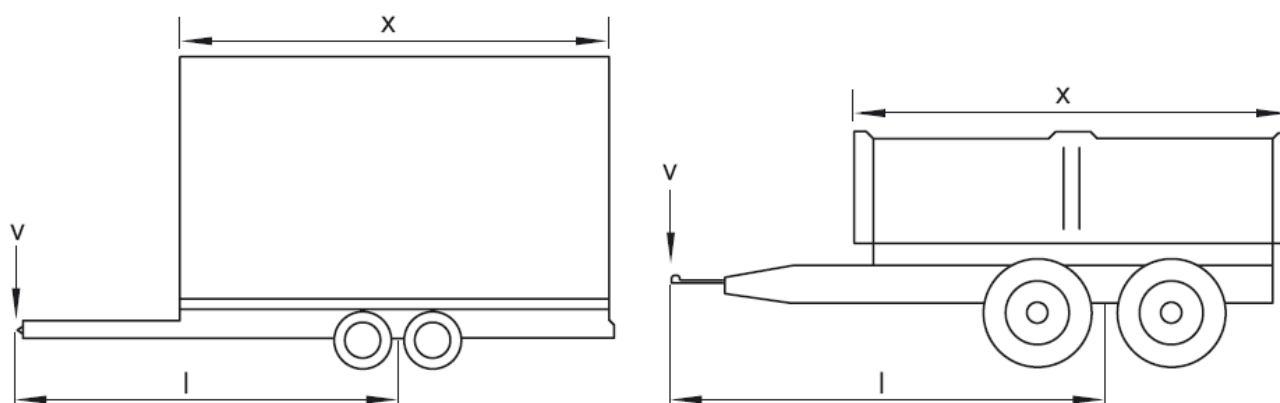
Длина кузовной надстройки прицепа и теоретическая длина дышла
